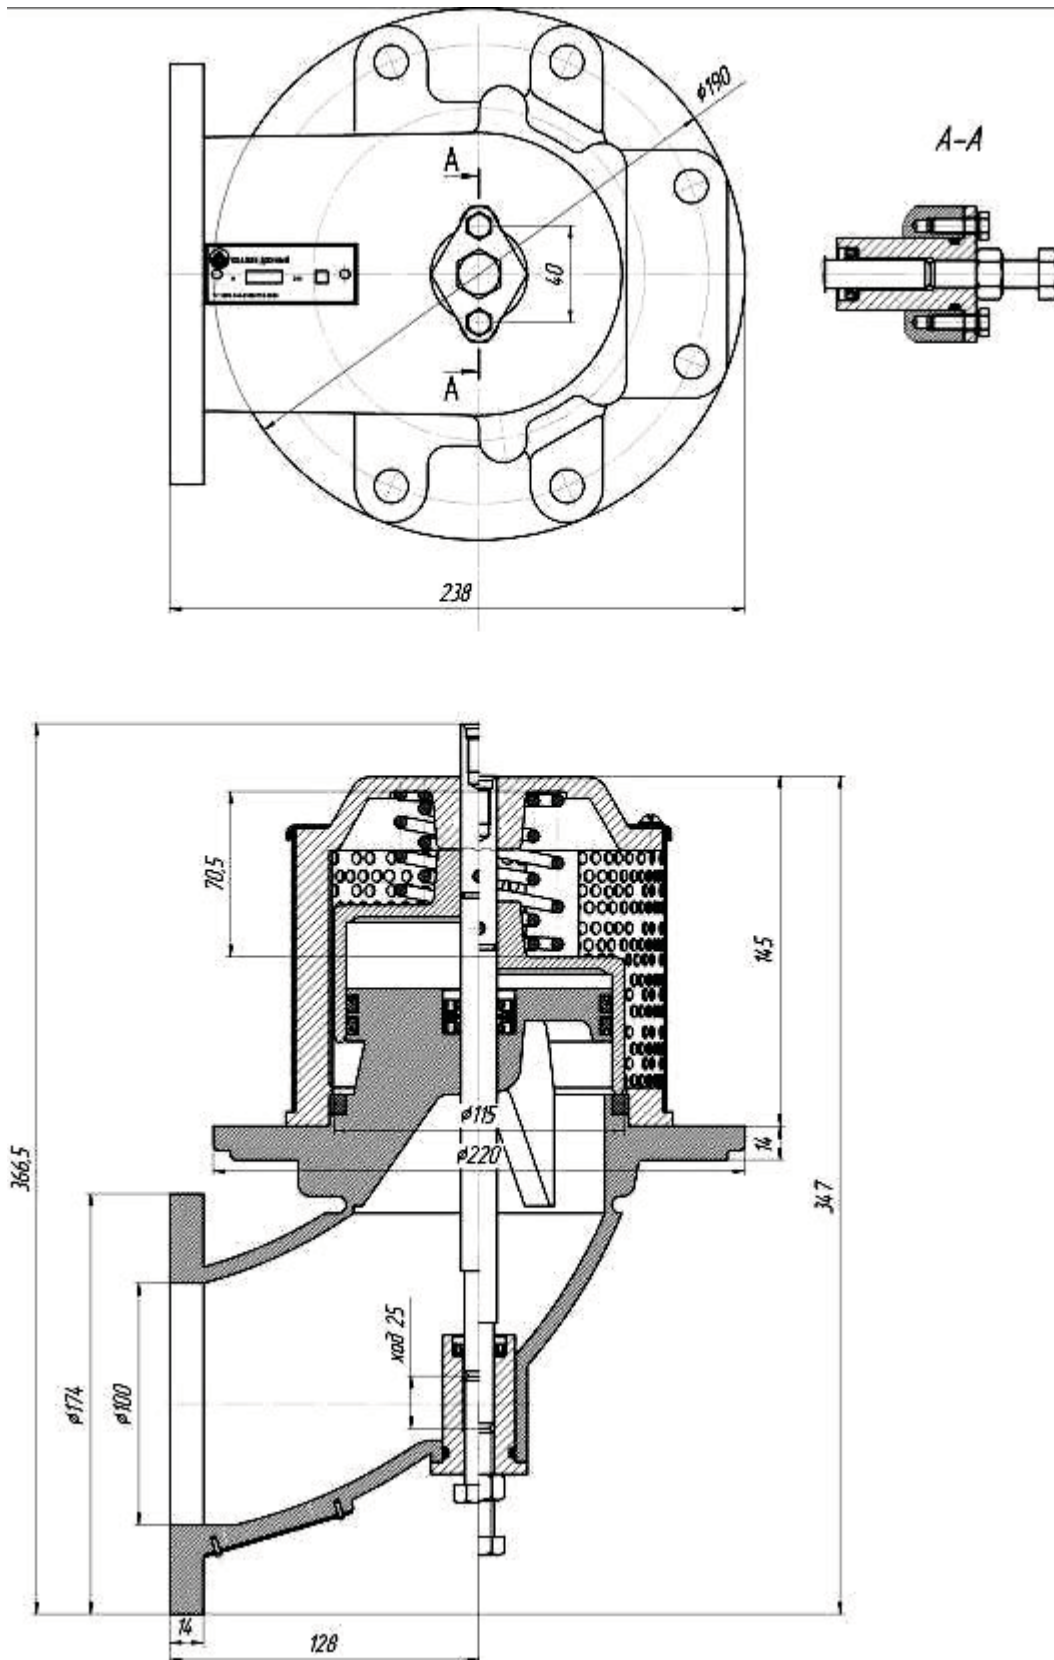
Типовой представитель: клапан донный пневматический с ручным дублированием
